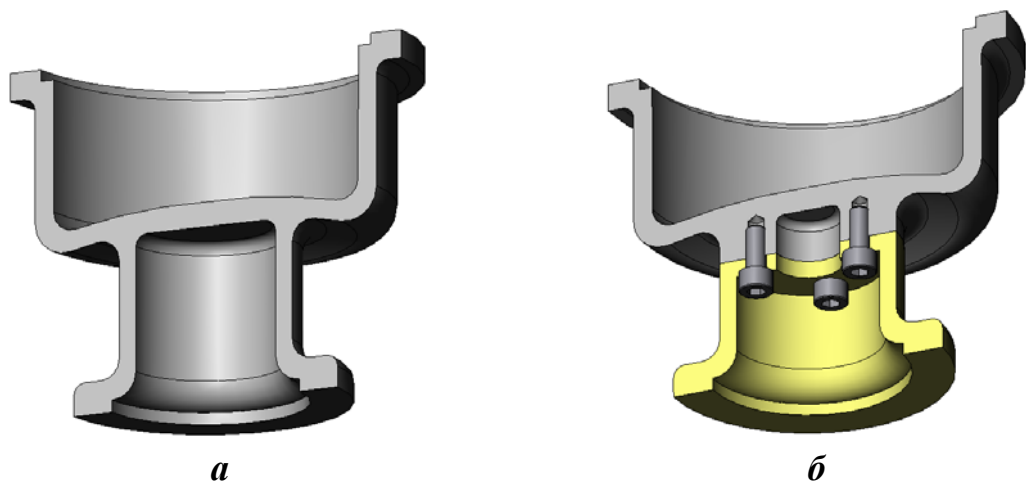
Конструкція суцільної (а) та складеної (б) заготовки
